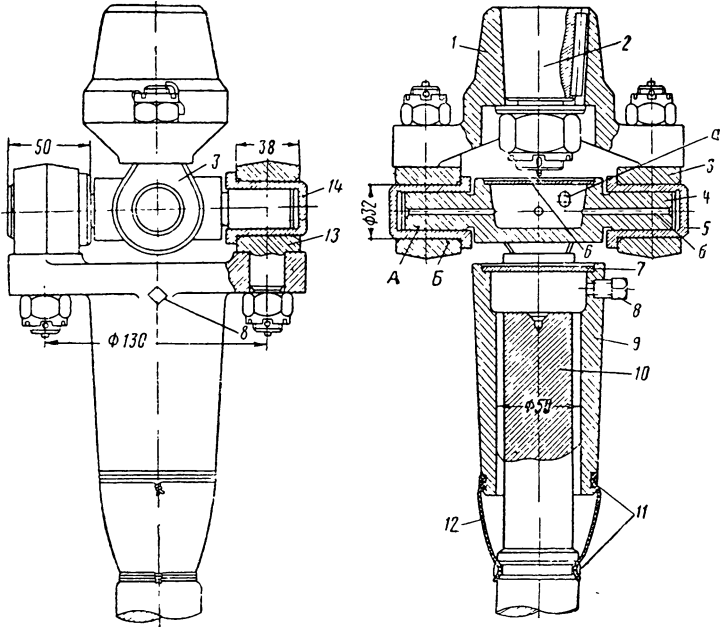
Карданное соединение промежуточного вала и вала вентилятора:
